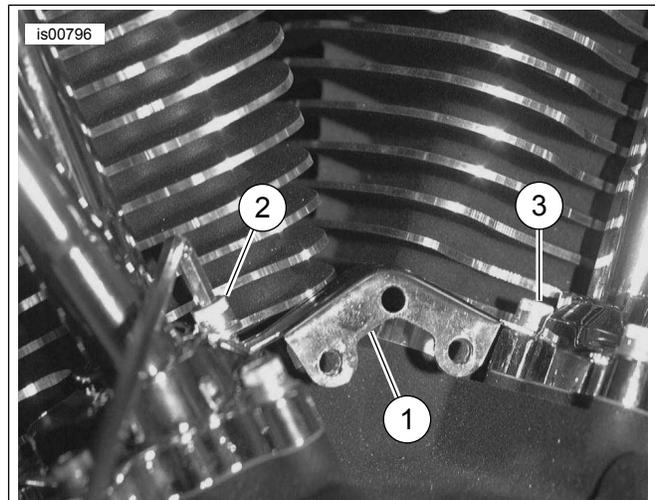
Vordere Stößeldeckelhalterung, eingebaut
